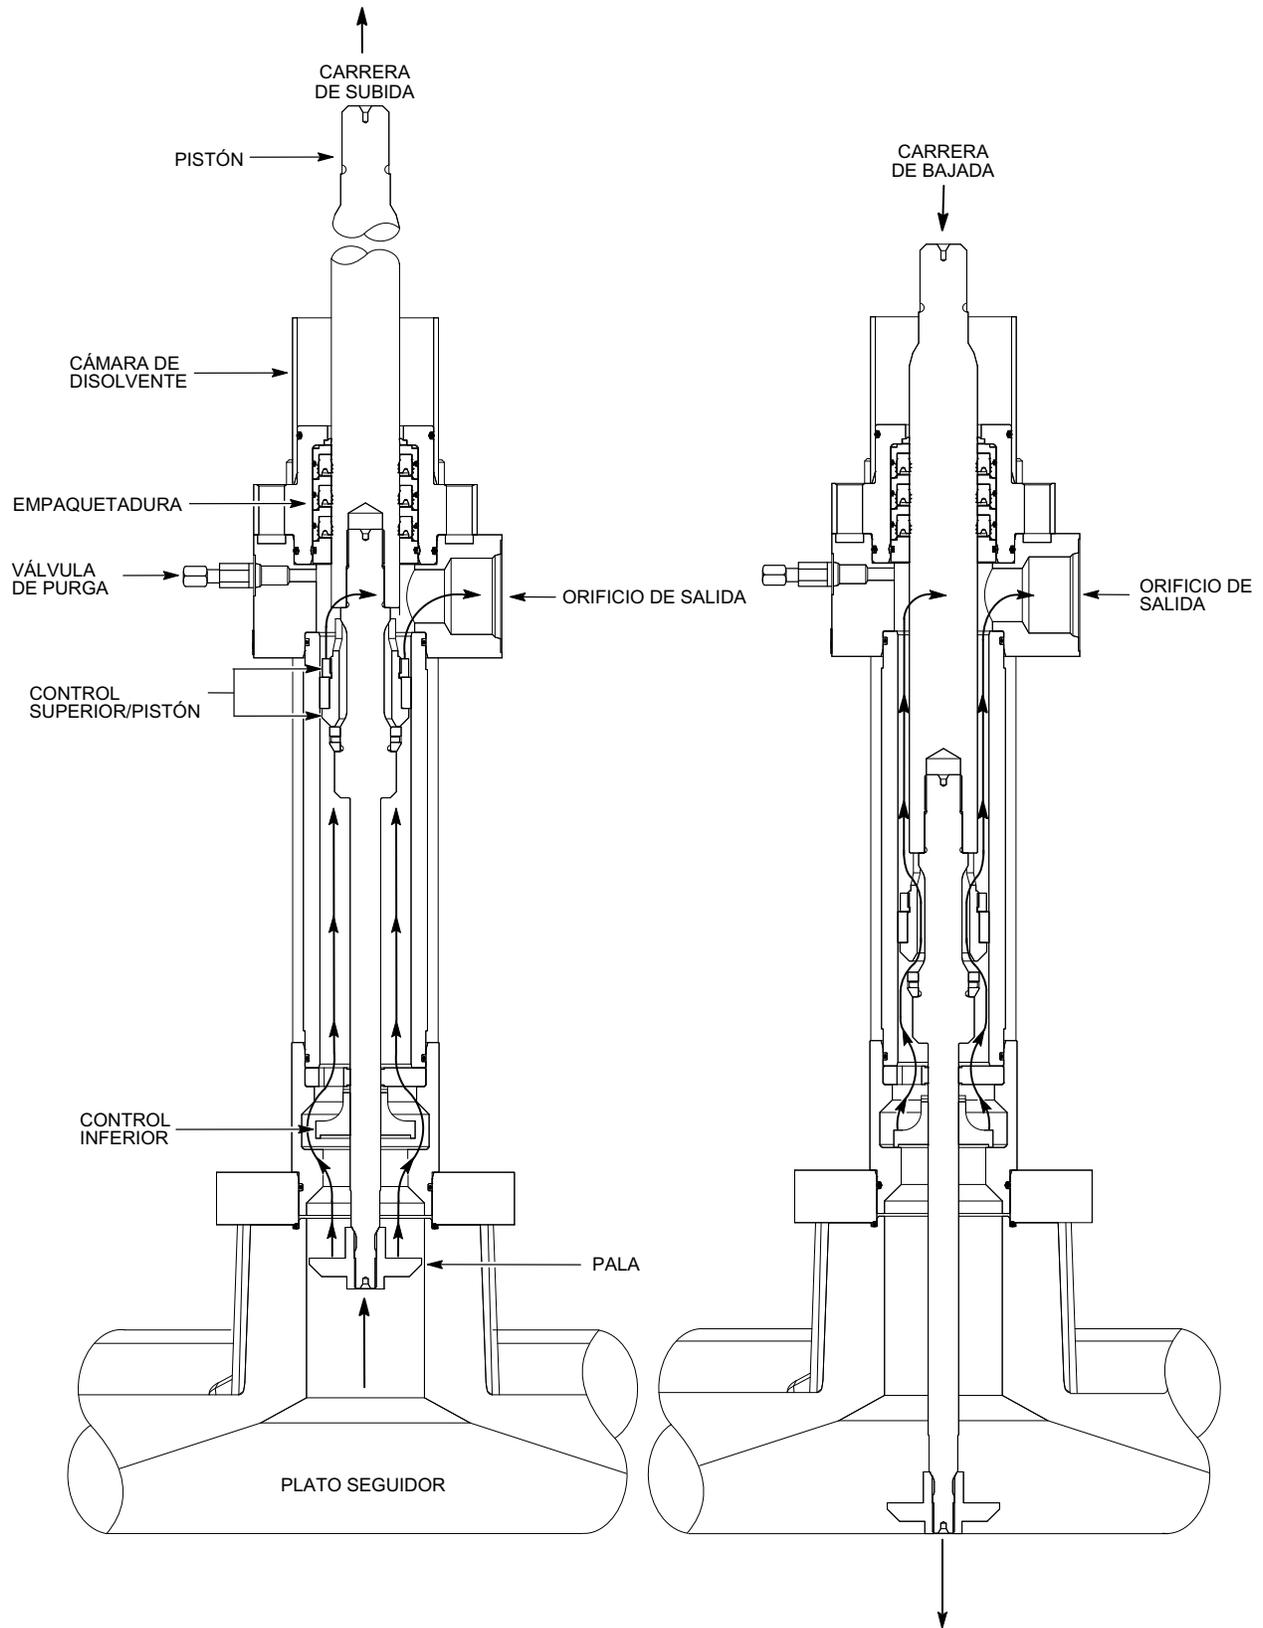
Secciones hidráulicas estándar y de temperatura acondicionada
